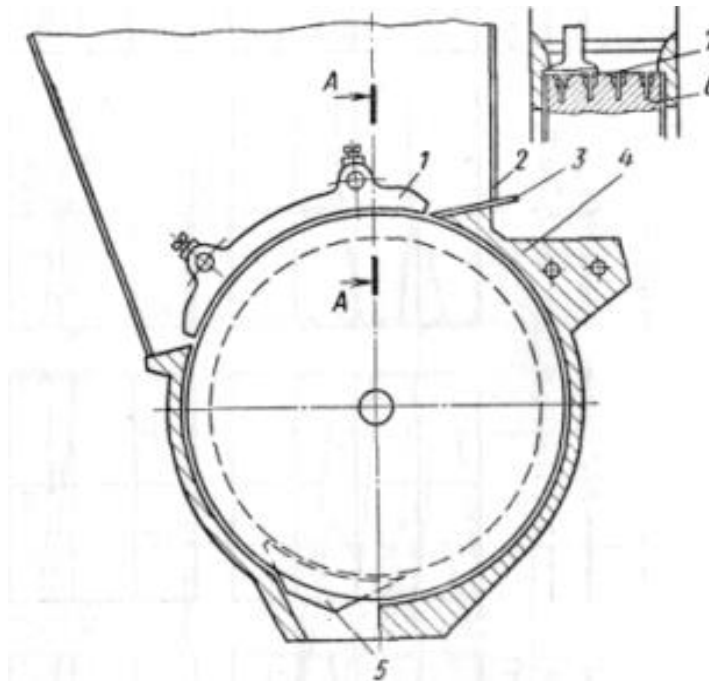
Висівний апарат сівалки «Палм Агроматік»: 1- заслінка; 2- бункер; 3- відсічний пристрій; 4- корпус; 5- виштовхувач; 6- висівний барабан; 7- осередки.
